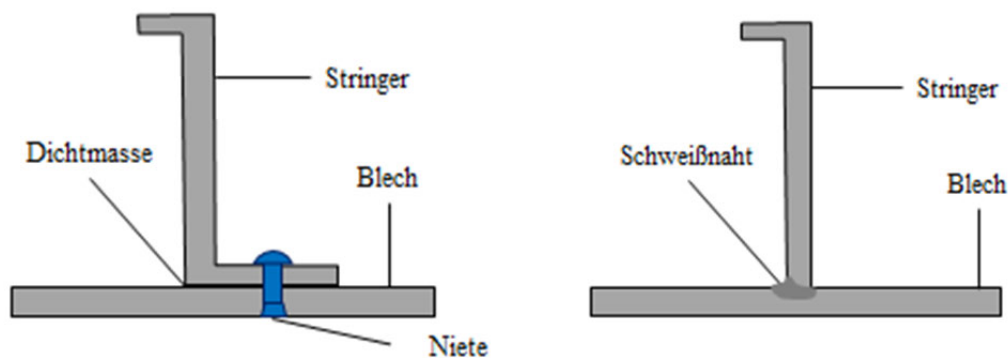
Gegenüberstellung der Flanschniet- und Laserstrahlschweißverbindung nach [32] Bei der Verschweißung der Blechteile kommt es jedoch durch die punktuelle Wärmeeinwirkung zu Spannungsentwicklungen im Material, die einen plastischen Verzug zur Folge haben. Dieser ist für die Anwendung in der Luftfahrtindustrie nicht akzeptabel und muss somit vor einer weiteren Verarbeitung der erzeugten Strukturen begradigt werden. Im Projekt DelasTi wird angestrebt diese notwendige Begradigung mittels Laserstrahl durchführbar zu machen. Die theoretische Betrachtung der Verzugswinkelbildung, sowie dessen Ansatz zur Begradigung wird im Folgenden erläutert.
